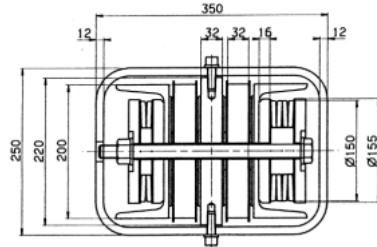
ユニット型免震用ブレーキダンパー断面図
